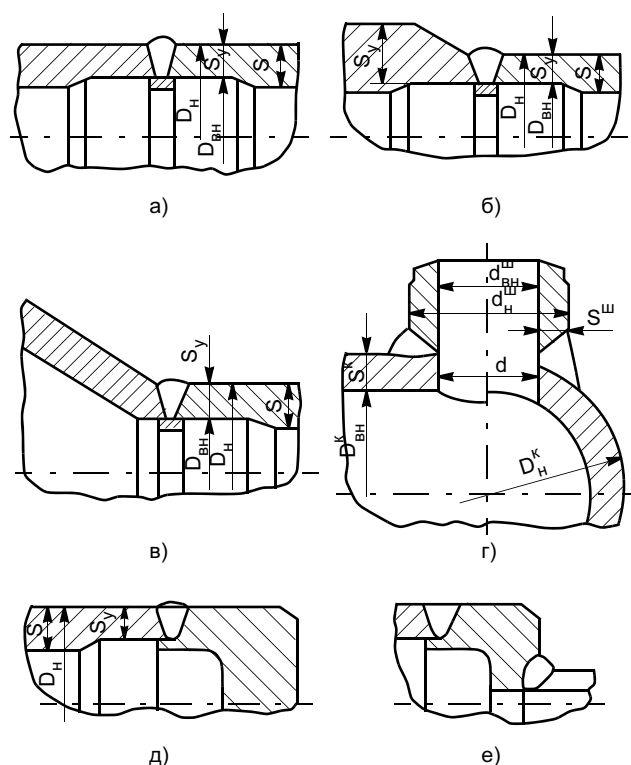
Типы сварных соединений паропроводов: а — стыковое сварное соединение трубных элементов с одинаковой толщиной стенки — СССР; б — стыковое сварное соединение разнотолщинных трубных элементов — СССР_{ртз}; в — стыковое сварное соединение трубы с коническим переходом — СССР_{кп}; г — тройниковое (штуцерное) сварное соединение — ТСС (ШСС); д — стыковое сварное соединение трубы с donышком — СССР_д; е — штуцерное сварное соединение патрубка с donышком — ШСС_д
